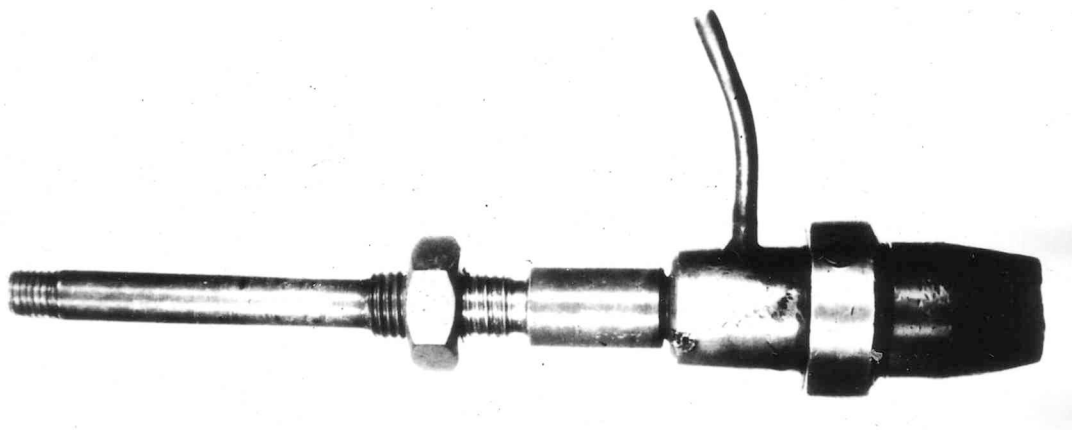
Зварювальний пальник до наплавочної головки ПАУ-1
